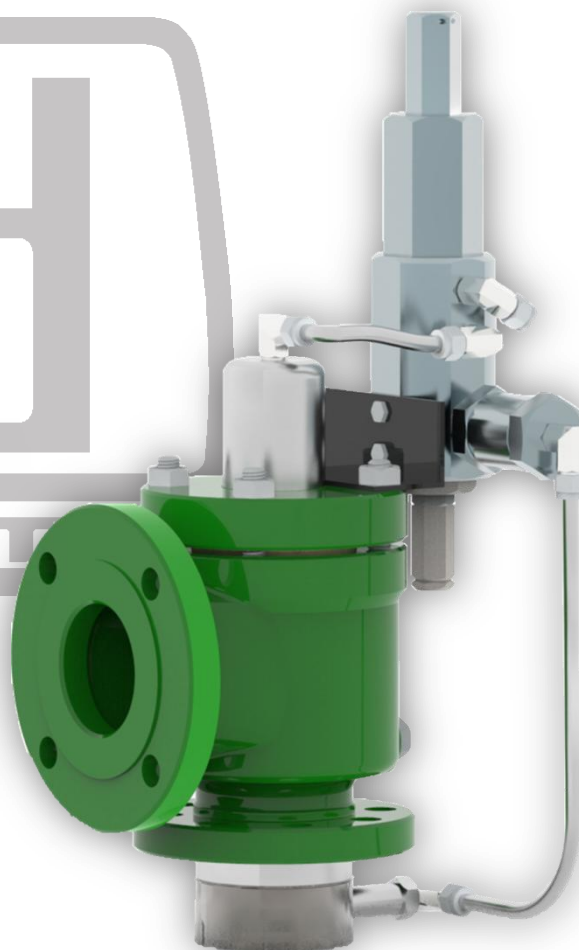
Válvula "DAP" con anillo sensor en posición de montaje.
